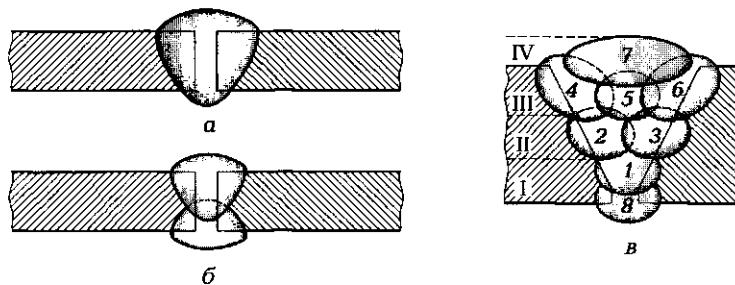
Строение сварных швов разного исполнения:
